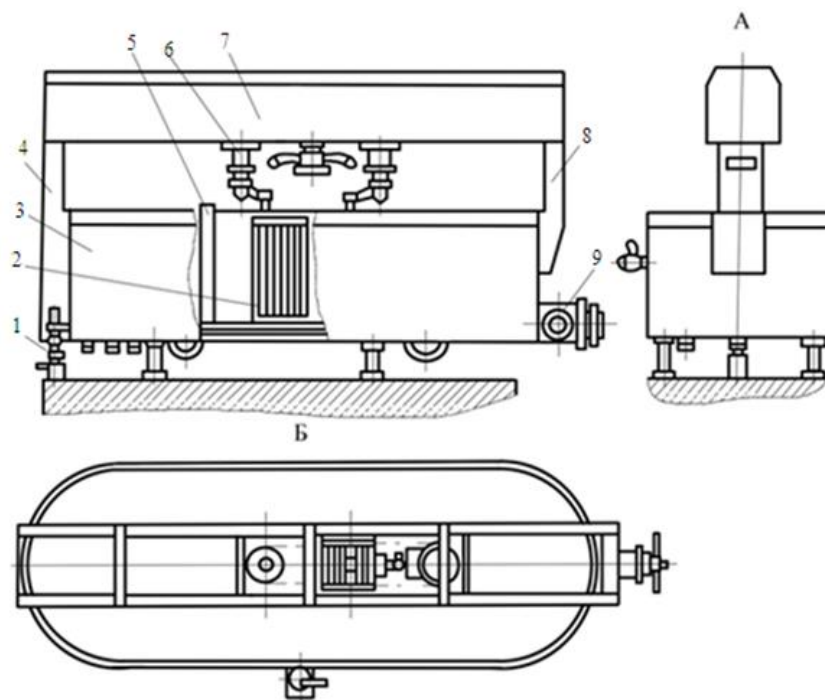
Сироробна ванна Д7-ОСА-1: 1 – домкрат; 2 – перемішувальний пристрій; 3 – корпус; 4, 8 – колона; 7 – мостова конструкція; 9 – запірний клапан
